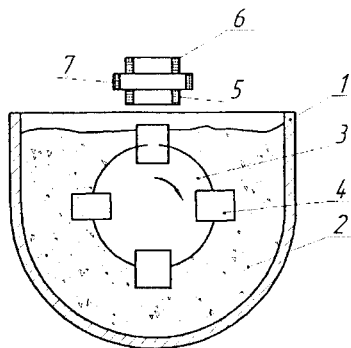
Принцип контроля поверхностного слоя ферромагнитных деталей 1 - контейнер; 2 - рабочая среда; 3 - барабан; 4 - обрабатываемая деталь; 5 - измерительный преобразователь; 6 - компенсационный преобразователь; 7 - катушка возбуждения.
